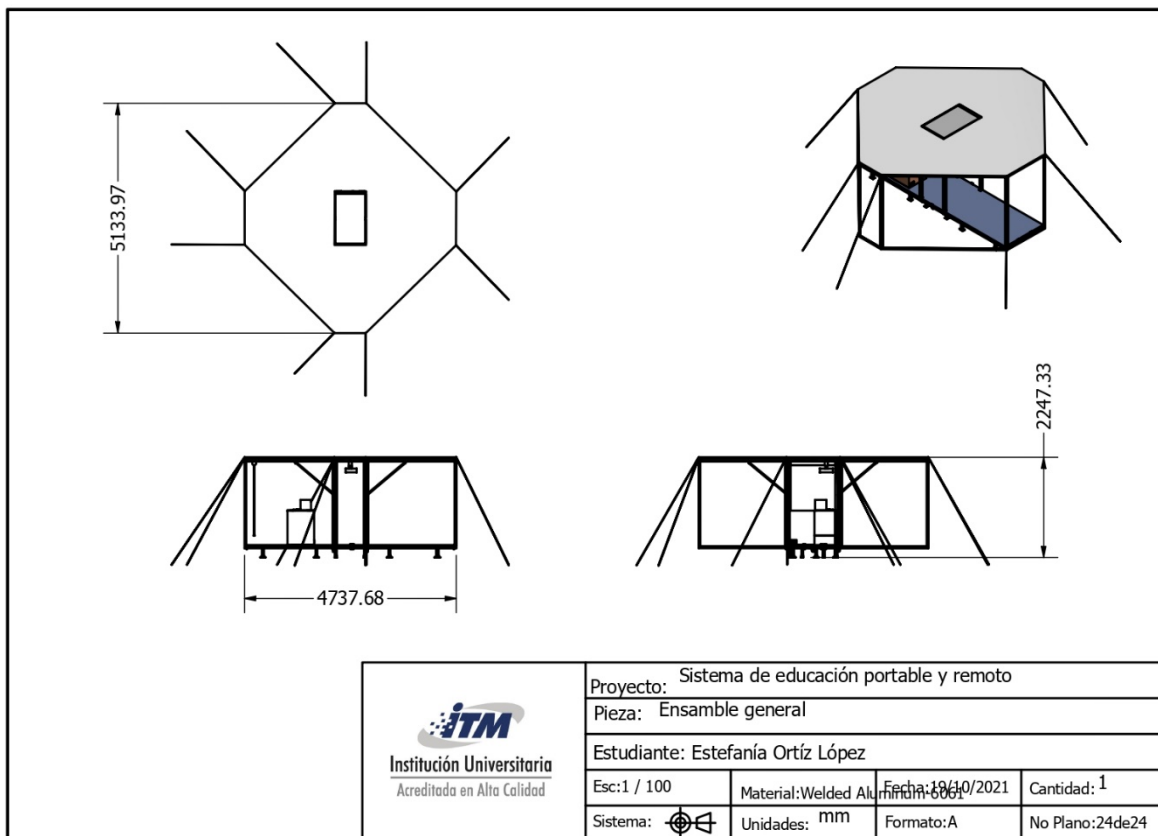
Plano general de ensamble de todas las piezas. Fuente: Elaboración propia
